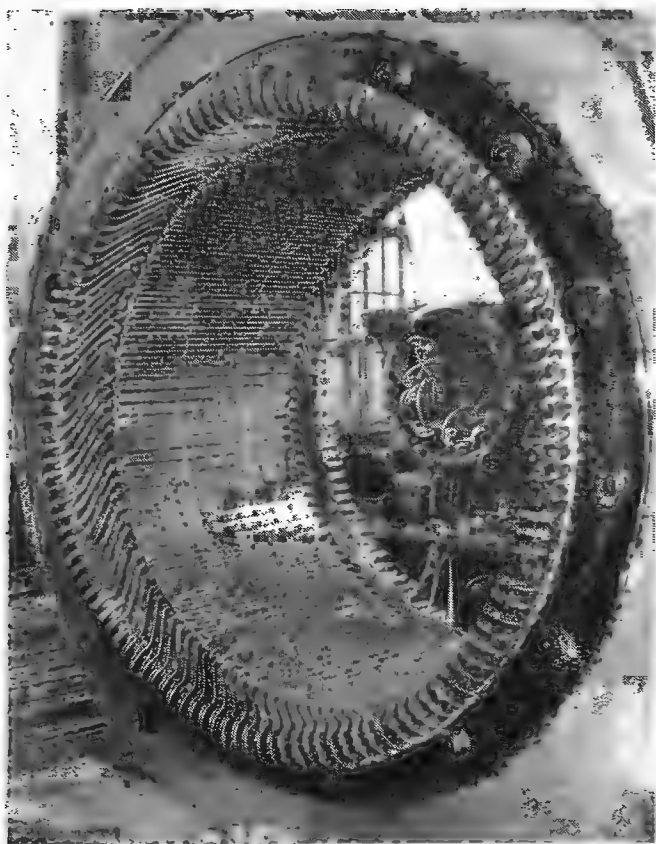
Двухслойная обмотка статора с петлевыми катушками одинакового шага (АЭГ).
